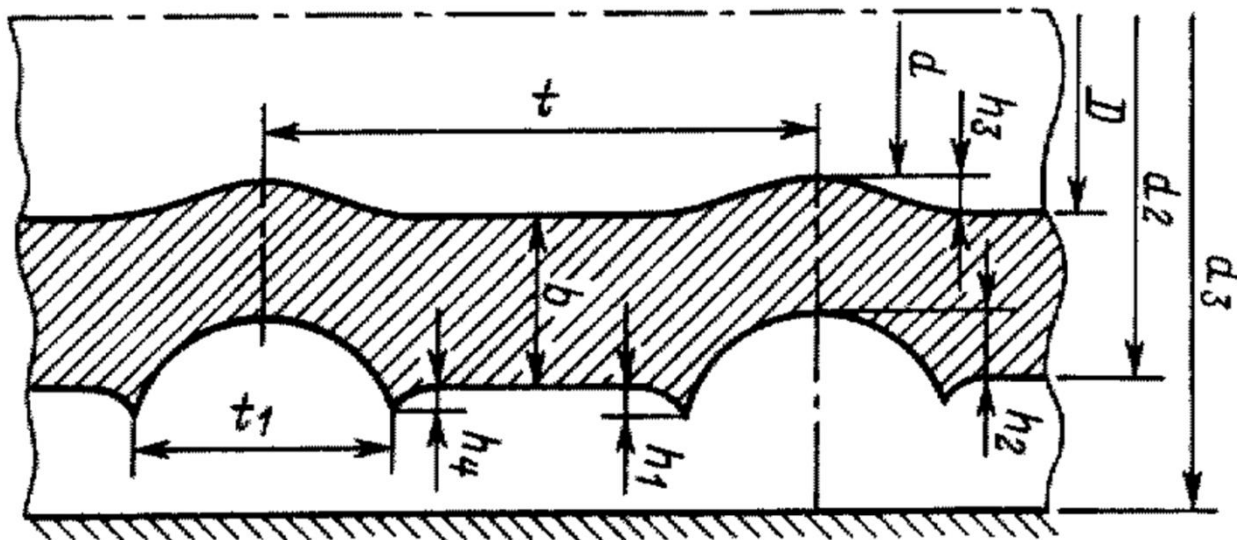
Фрагмент конструкции трубы с накатанными комбинированными турбулизаторами типа "выступ—канавка" [17, 4].
